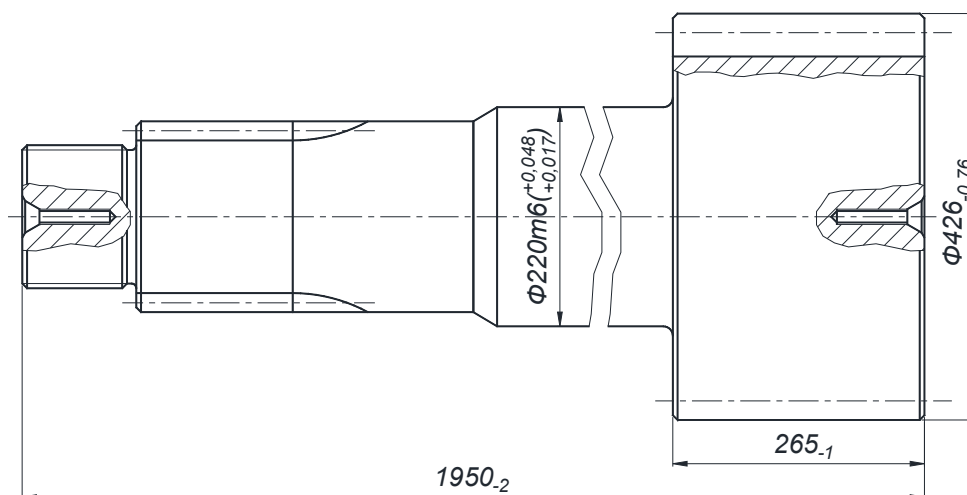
Вал шестерня экскаватора ЭКГ-8
